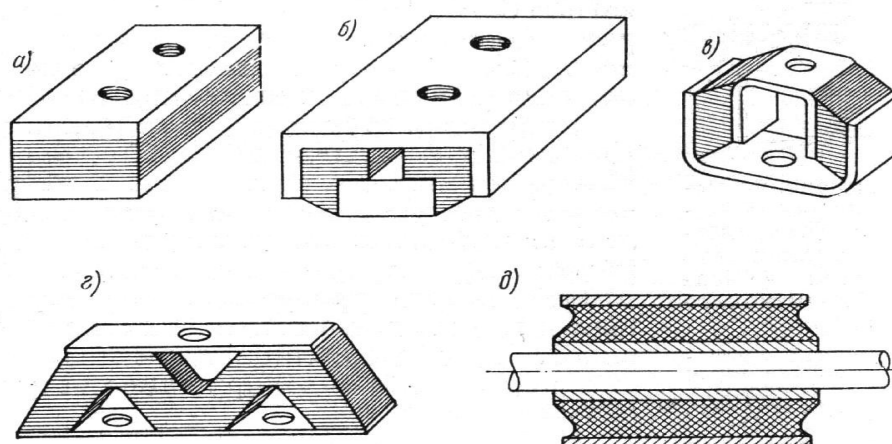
Конструкции сварных резино-металлических амортизаторов
